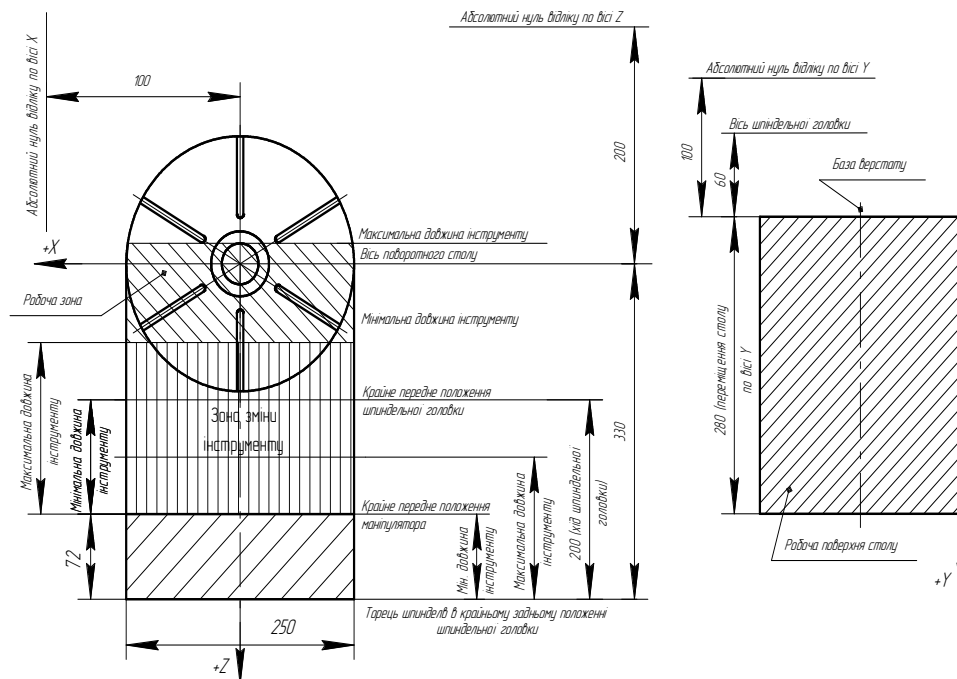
Визначення робочої зони для обробки деталі на верстаті MC 12-250M
